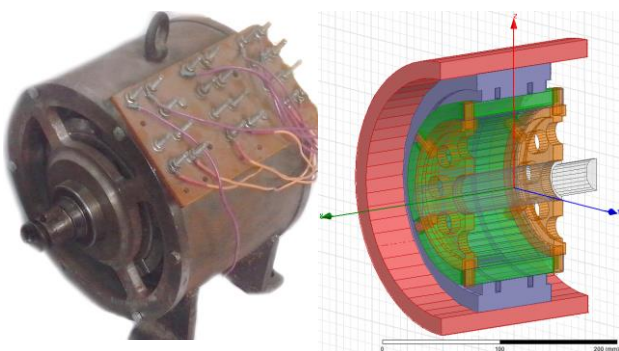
Конструкція 6-пазового ДРК з габаритними розмірами 250x250x170 мм
